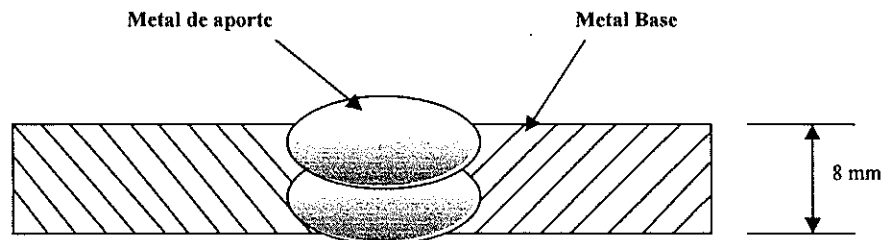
ESQUEMA DE LA UNION SOLDADA SIN FALLA
